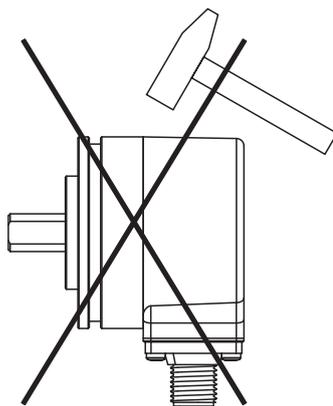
Montageansicht – nicht mit dem Hammer ausrichten
